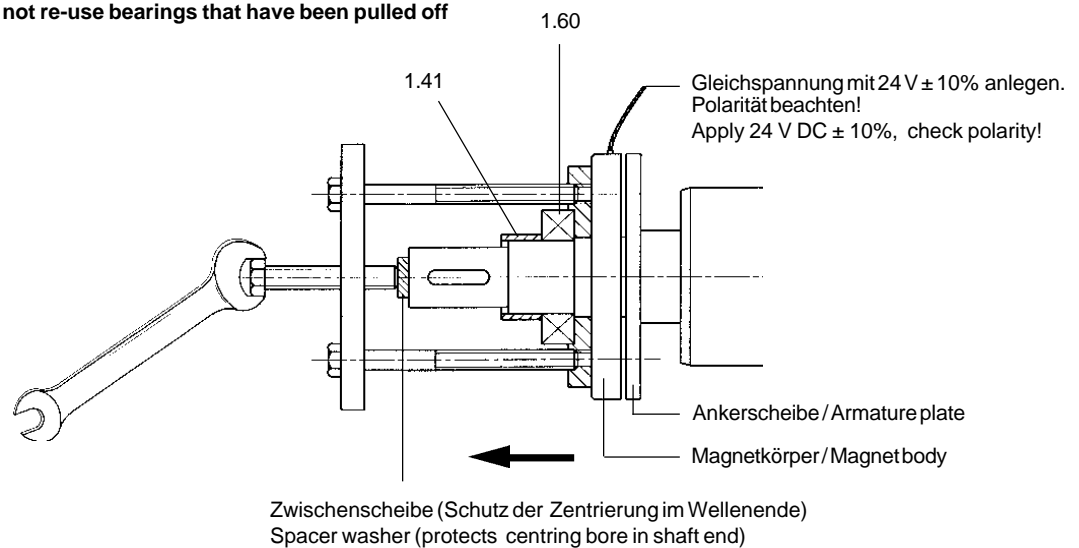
Lagerwechsel bei Motoren mit Bremse / Changing bearings on motors with brake
